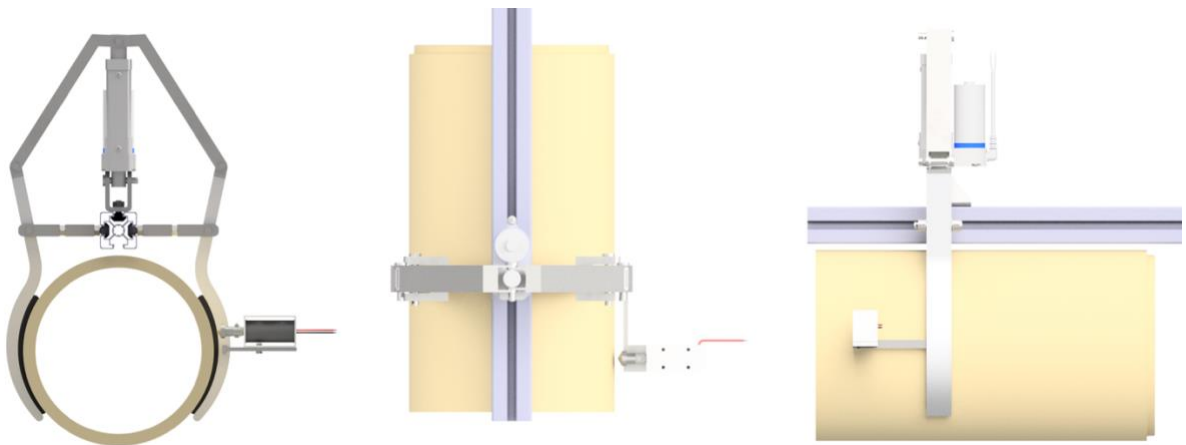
Finální konstrukce pevného návrhu – 3D pohled a návrh v otevřeném stavu
